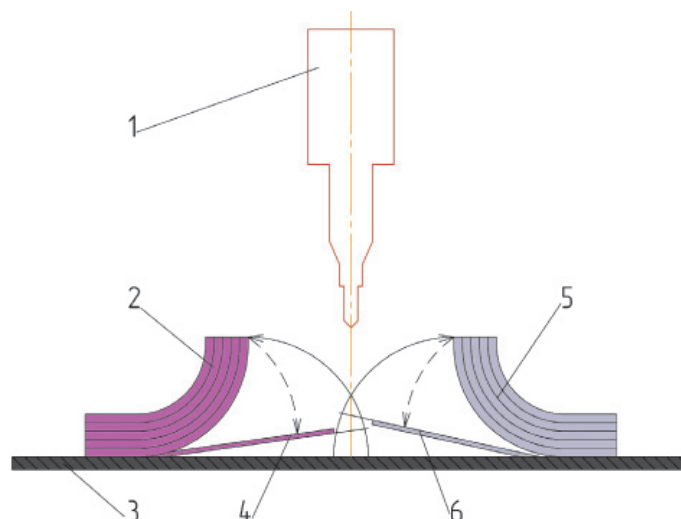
Принципиальная схема устройства для сварки блоков геолент:
